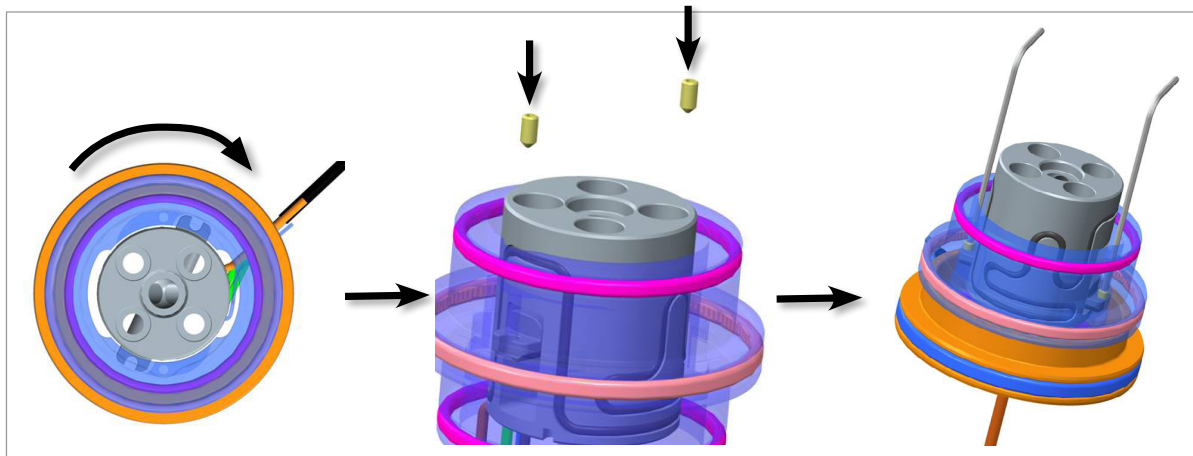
Blocco del gruppo pistone e del supporto del perno della valvola
